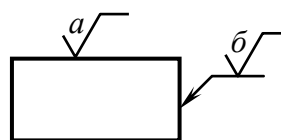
Пример условного обозначения шероховатости поверхности
